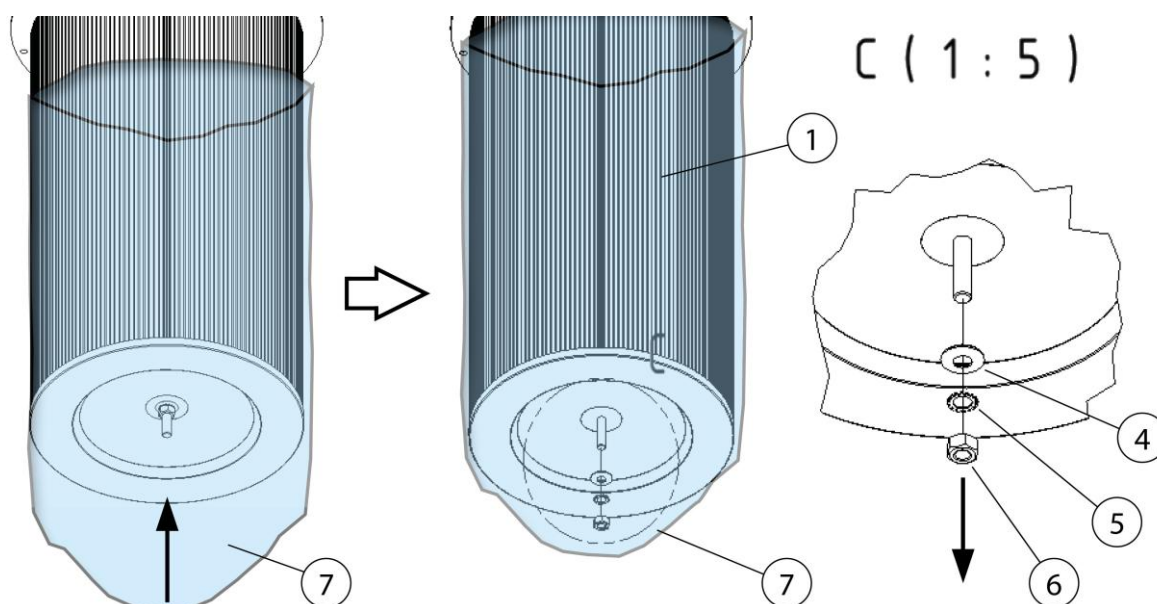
Remplacement du filtre - démontage de la cartouche filtrante
